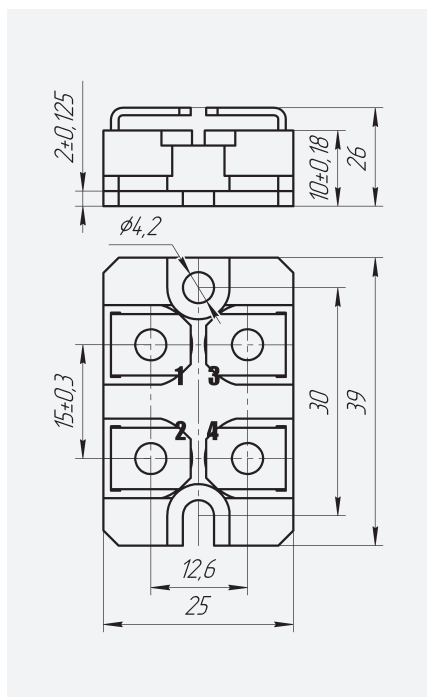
Габаритный чертеж резистора P1-150M (исполнения 2, 4) и наборов резисторов NP1-82 (исполнение 1)
